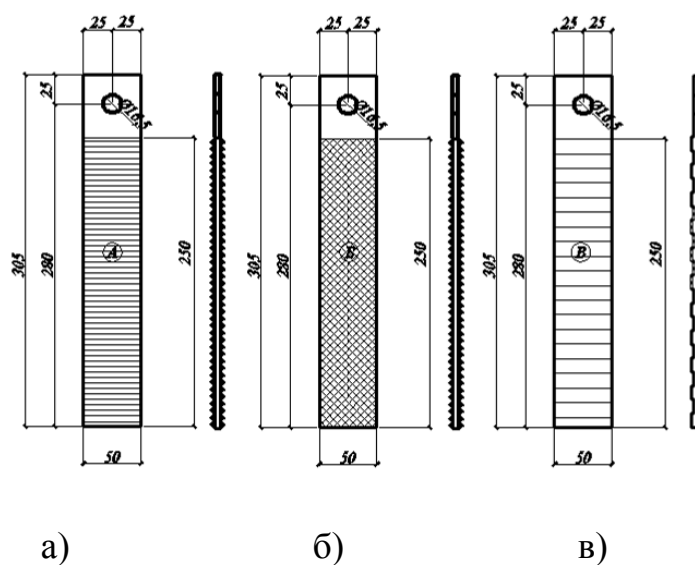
Типы механической обработки поверхности пластин:
